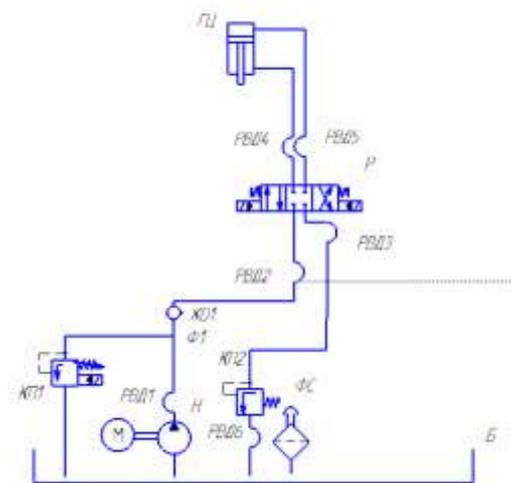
Существующая гидравлическая схема рабочей головки зачистного станка
